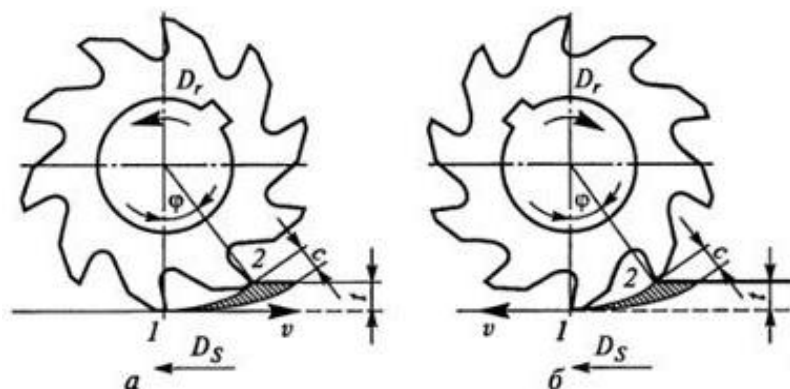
Методы фрезерования: а – встречное, б – попутное
